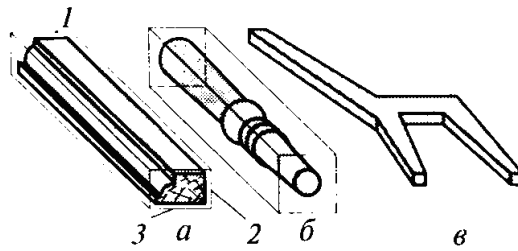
Форма заготівок і деталей, оброблюваних на деревообробних верстатах: *а* – призматична; *б* – тіла обертання; *в* – складна; 1 – упорна поверхня; 2 – напрямна поверхня; 3 – головна поверхня
